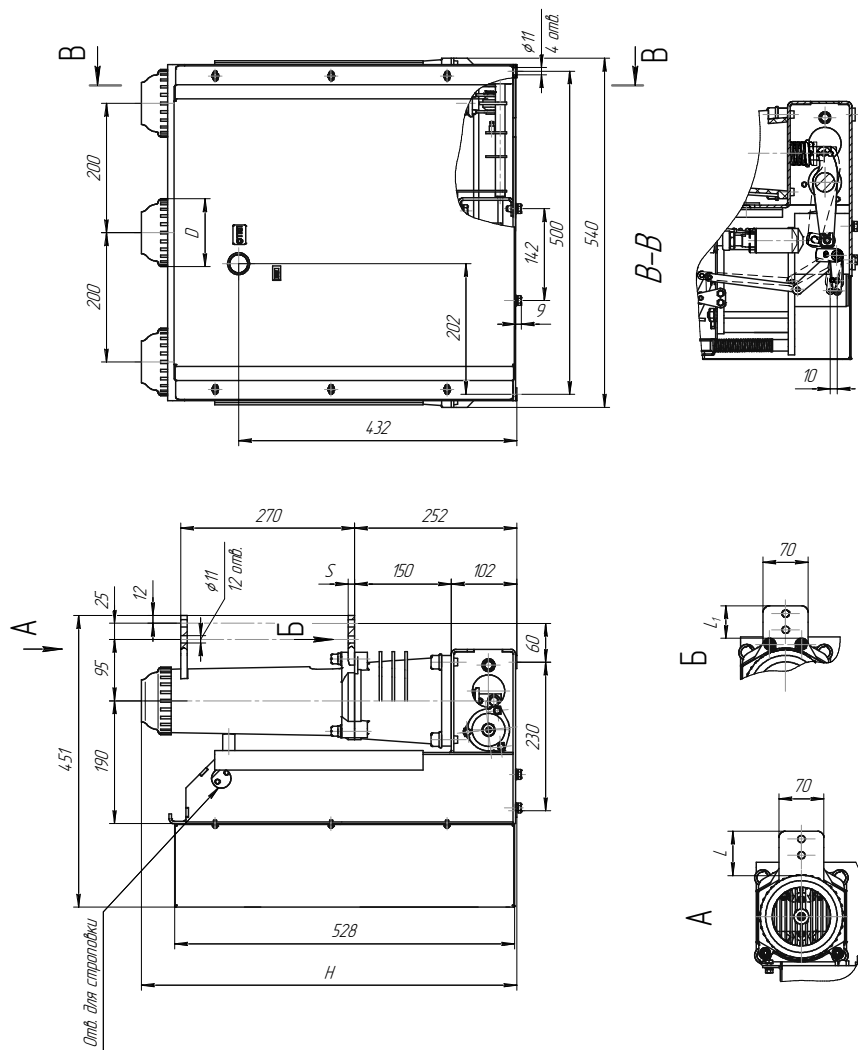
Габаритные, присоединительные и установочные размеры выключателя типа ВВУ-СЭЩ-Э-10-20(31,5)/ η (СЭЩ-70)
